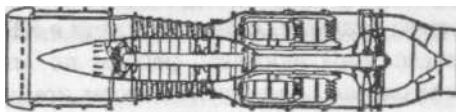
Турбореактивный двигатель ТР-1 [54]
